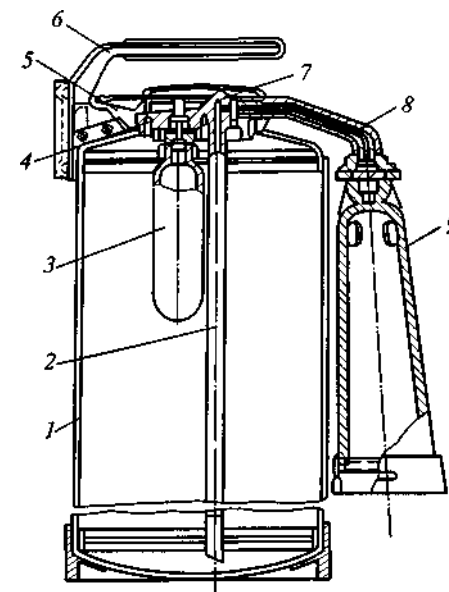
Пенный огнетушитель ОВП-10: 1 — стальной корпус; 2 — сифонная трубка; 3 — баллон для газа; 4 — крышка с запорно-пусковым устройством; 5 — пусковой рычаг; 6 — рукоятка; 7 — мембрана; 8 — напорные трубки; 9 — раструб
